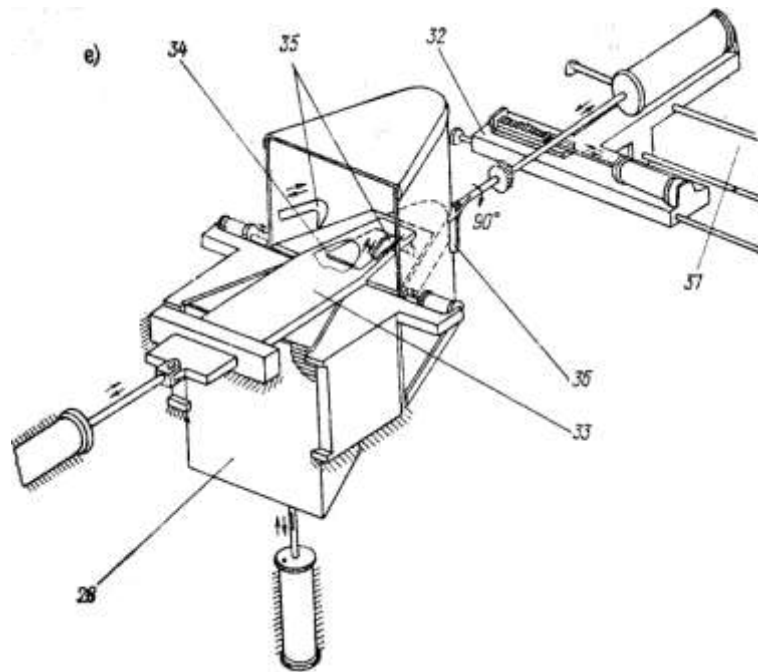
Схема автоматизированной линии сборки в сварки ковшей
